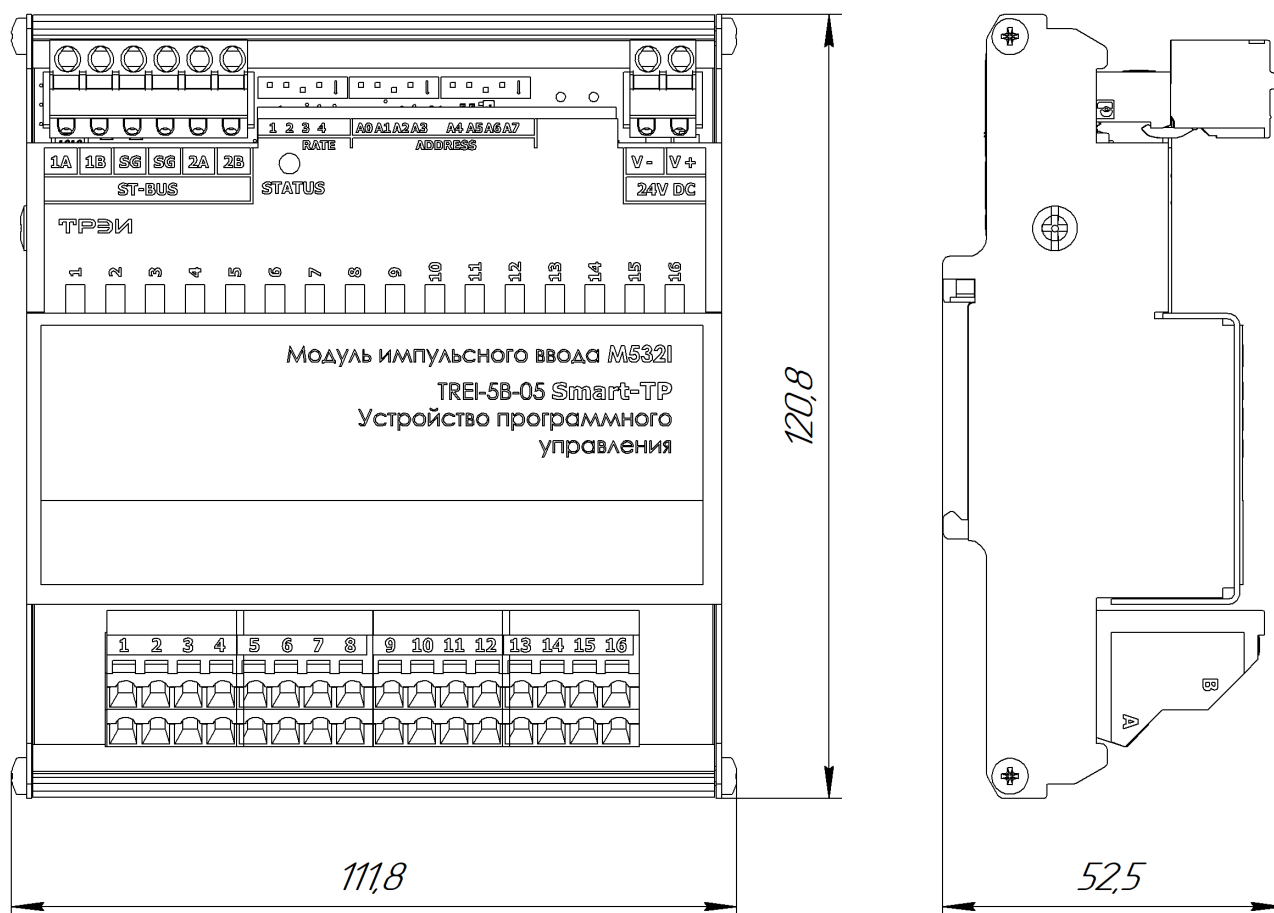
Чертеж общего вида M532I с указанием габаритных и присоединительных размеров
